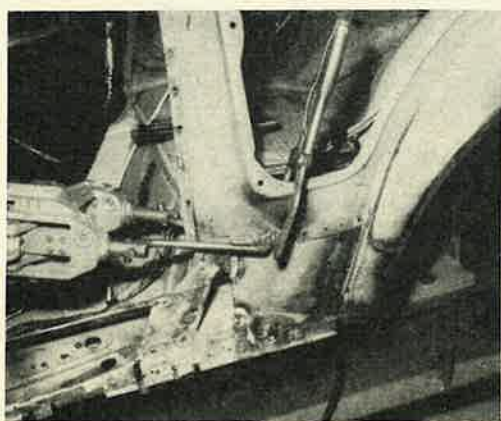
Soudage par résistance de la doublure de panneau de côté sur gousset renfort latéral gauche. Pince ARO 169 A (photo R.T.C.).
